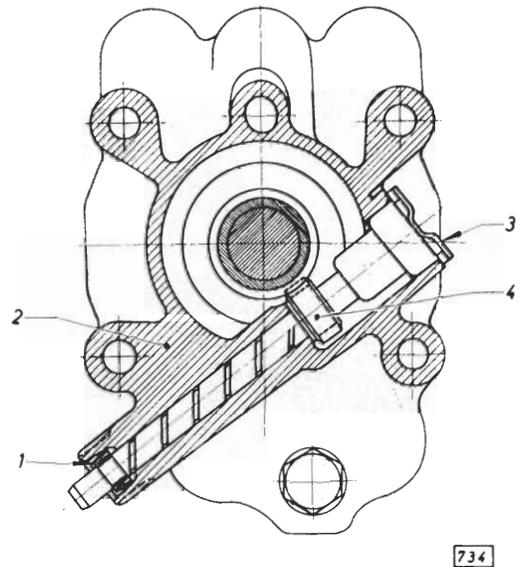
Tachometerschraubenrad in Getriebegehäuseendstück eingebaut
